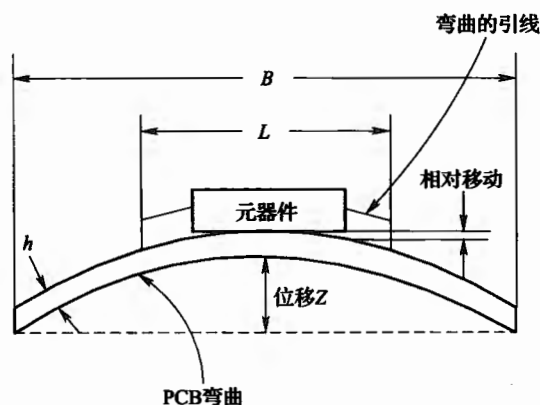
当 PCB 受激谐振时轴向引出的器件引线将会弯曲
